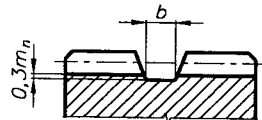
Размеры канавок для выхода червячных фрез
